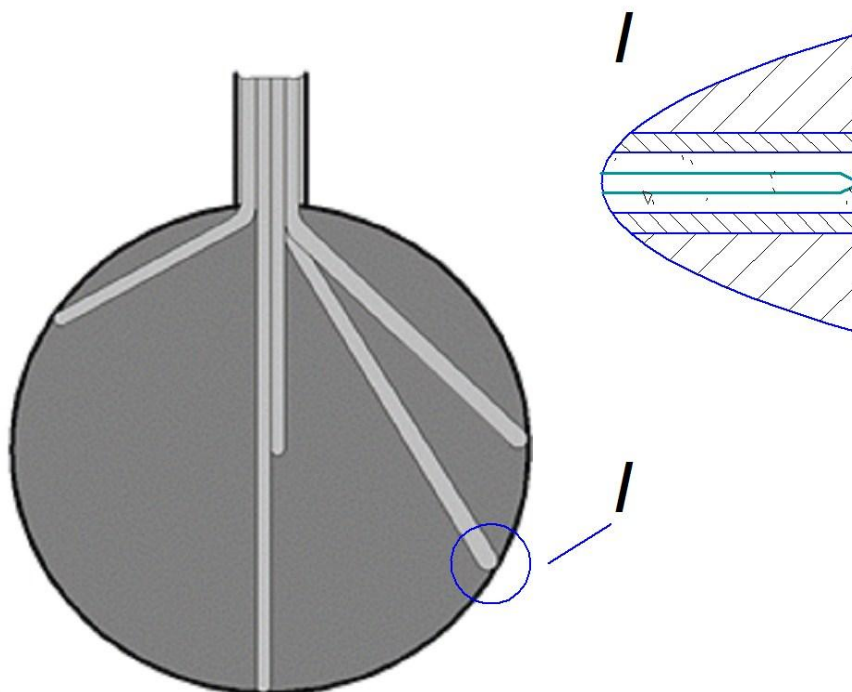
Схема крепления термопар к поверхности шара лазерной сваркой
